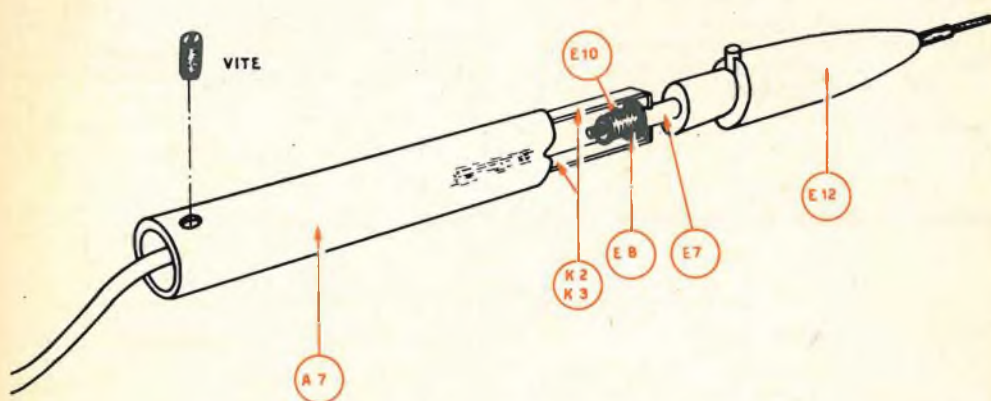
Puntale UNI-PROBE a montaggio quasi ultimato.
